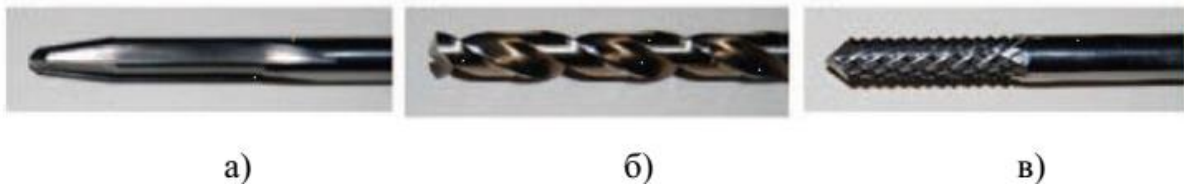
Используемые инструменты: а) периметр, б) спиральное сверло и в) фрезерный станок.
